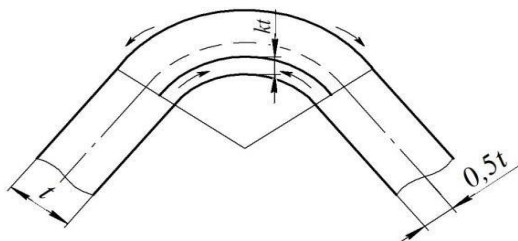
Теоретичне переміщення нейтральної вісь при згинанні заготовки
